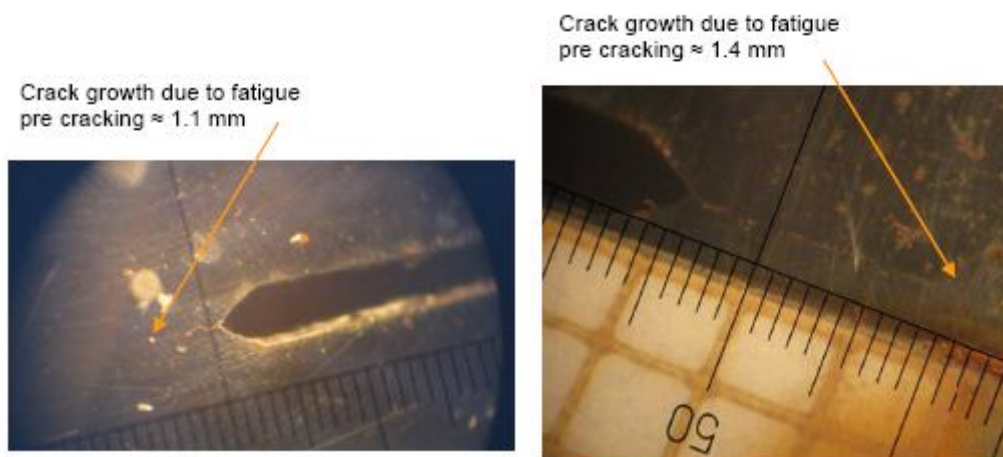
Dimensione finale del crack alla superficie per i due provini cruciformi
